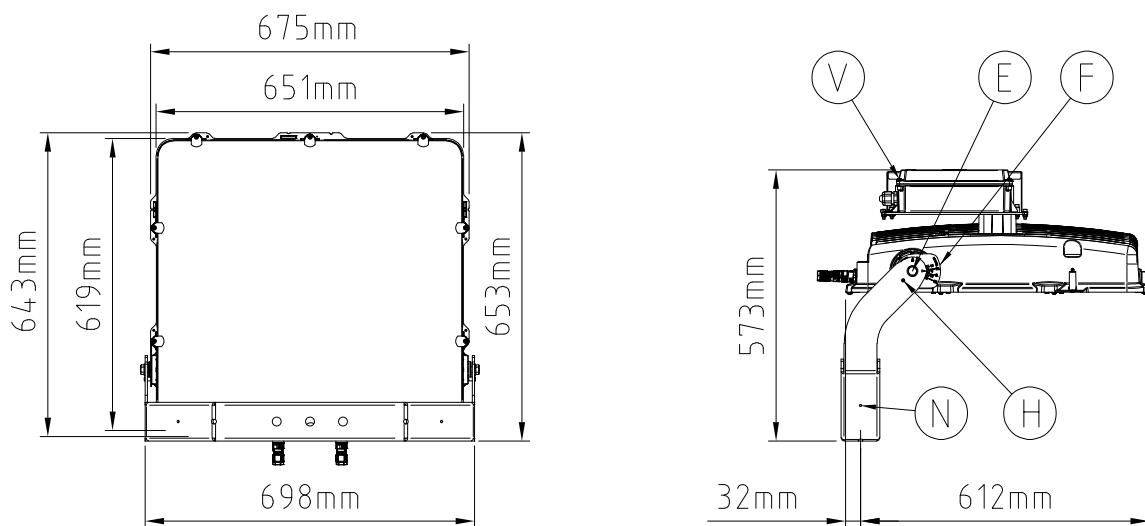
LEDMASTER ONE - Driver esterno a bordo 1 driver | *External driver on board 1 driver
